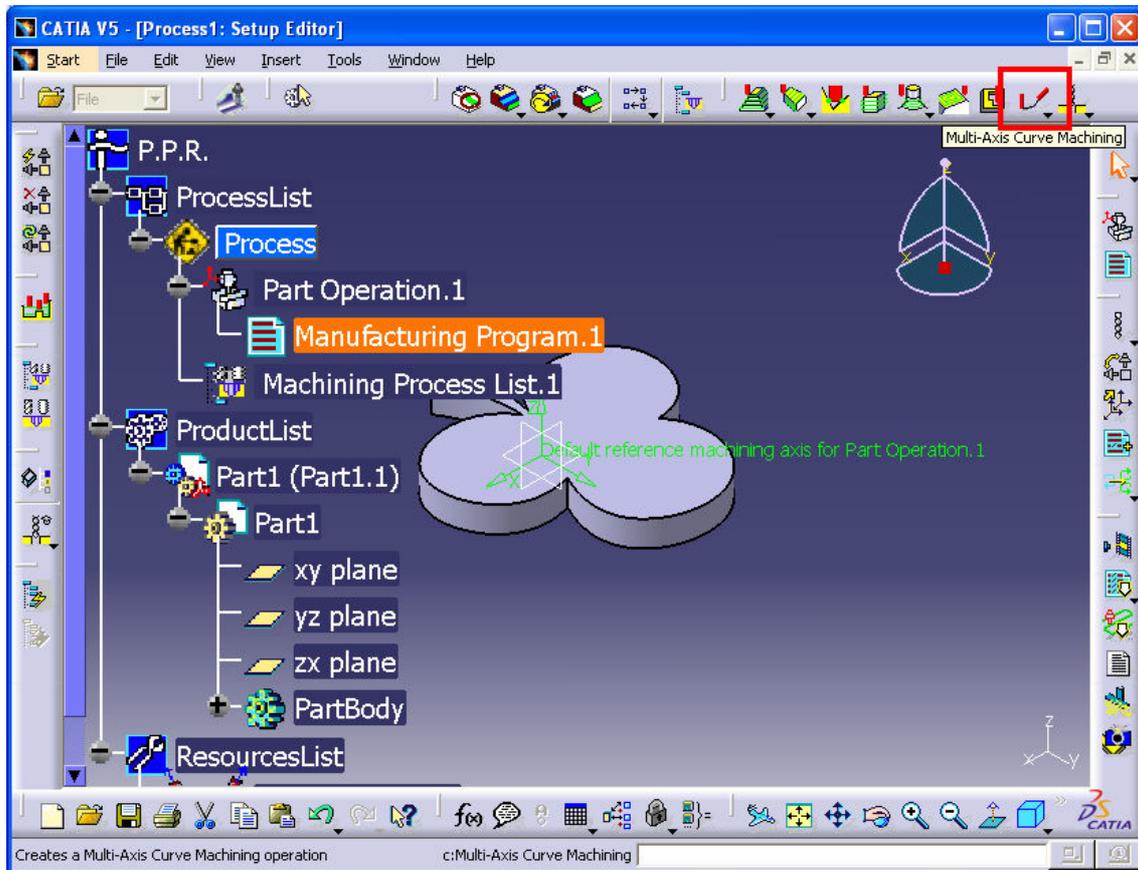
Herramienta de CN: Multi-Axis Curve Machining.
